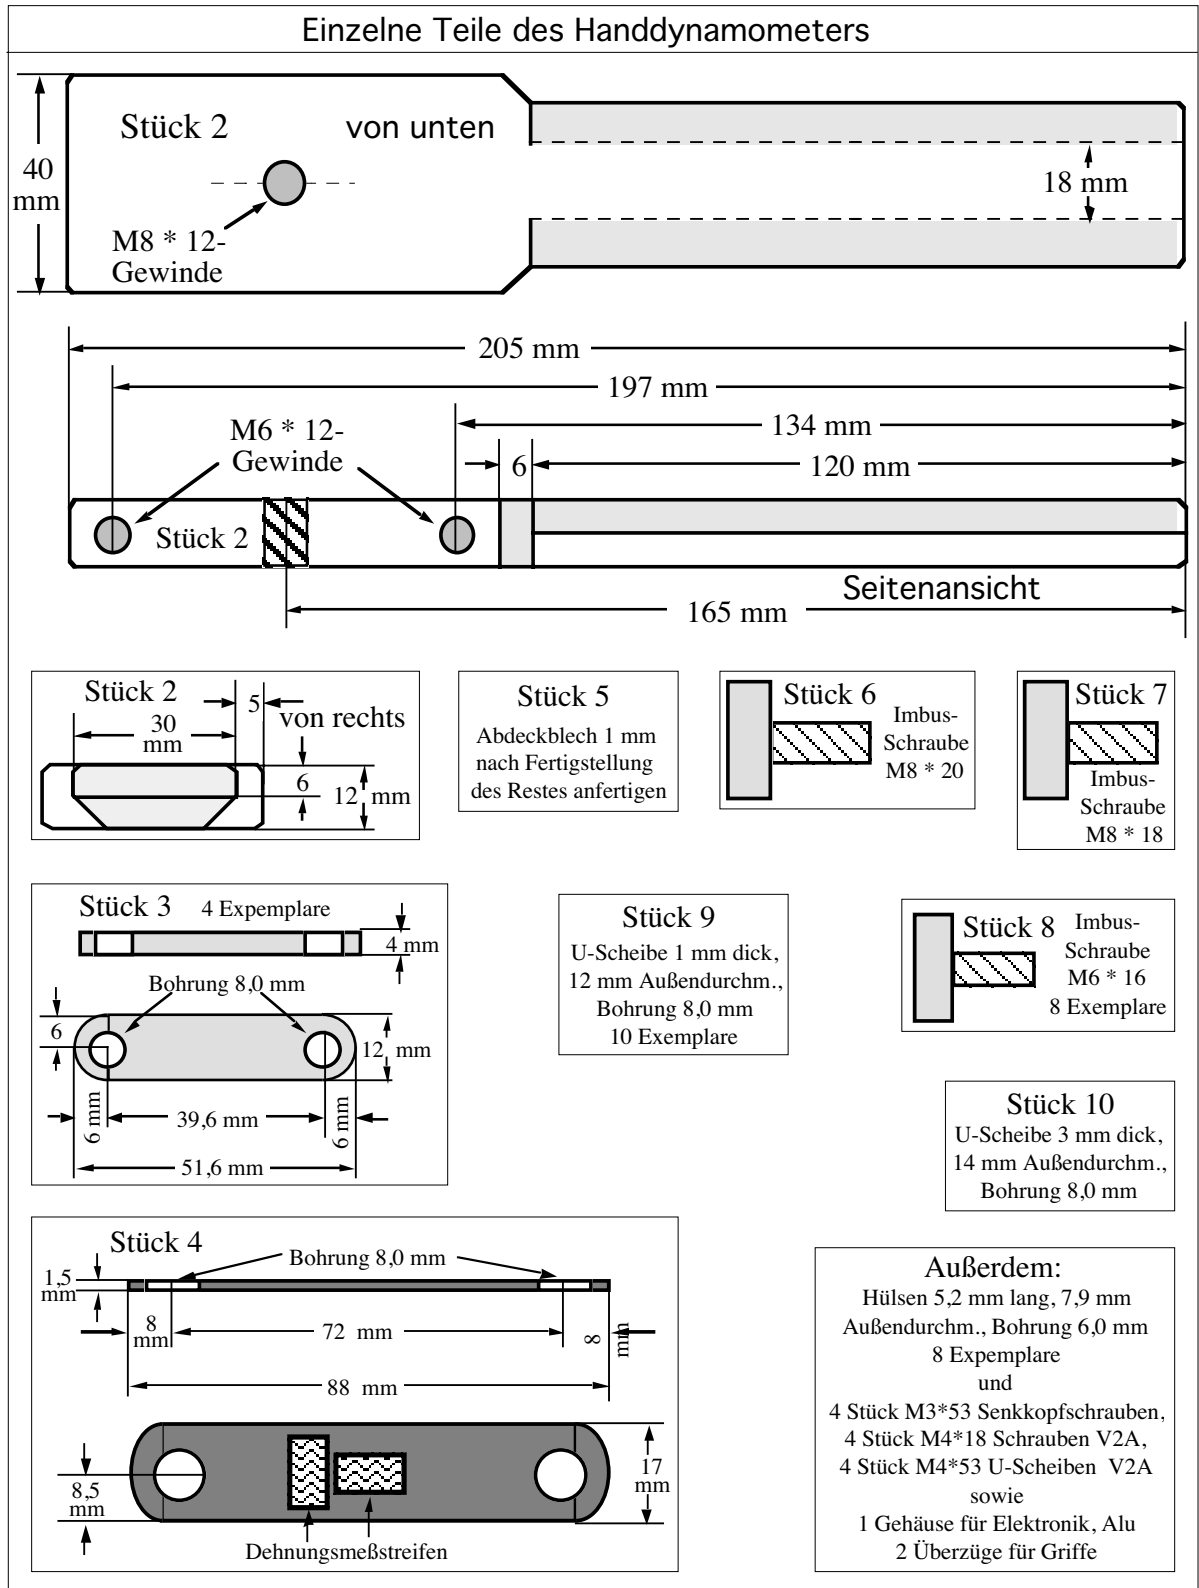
Konstruktionszeichnungen von Einzelteilen des Handdynamometers.
